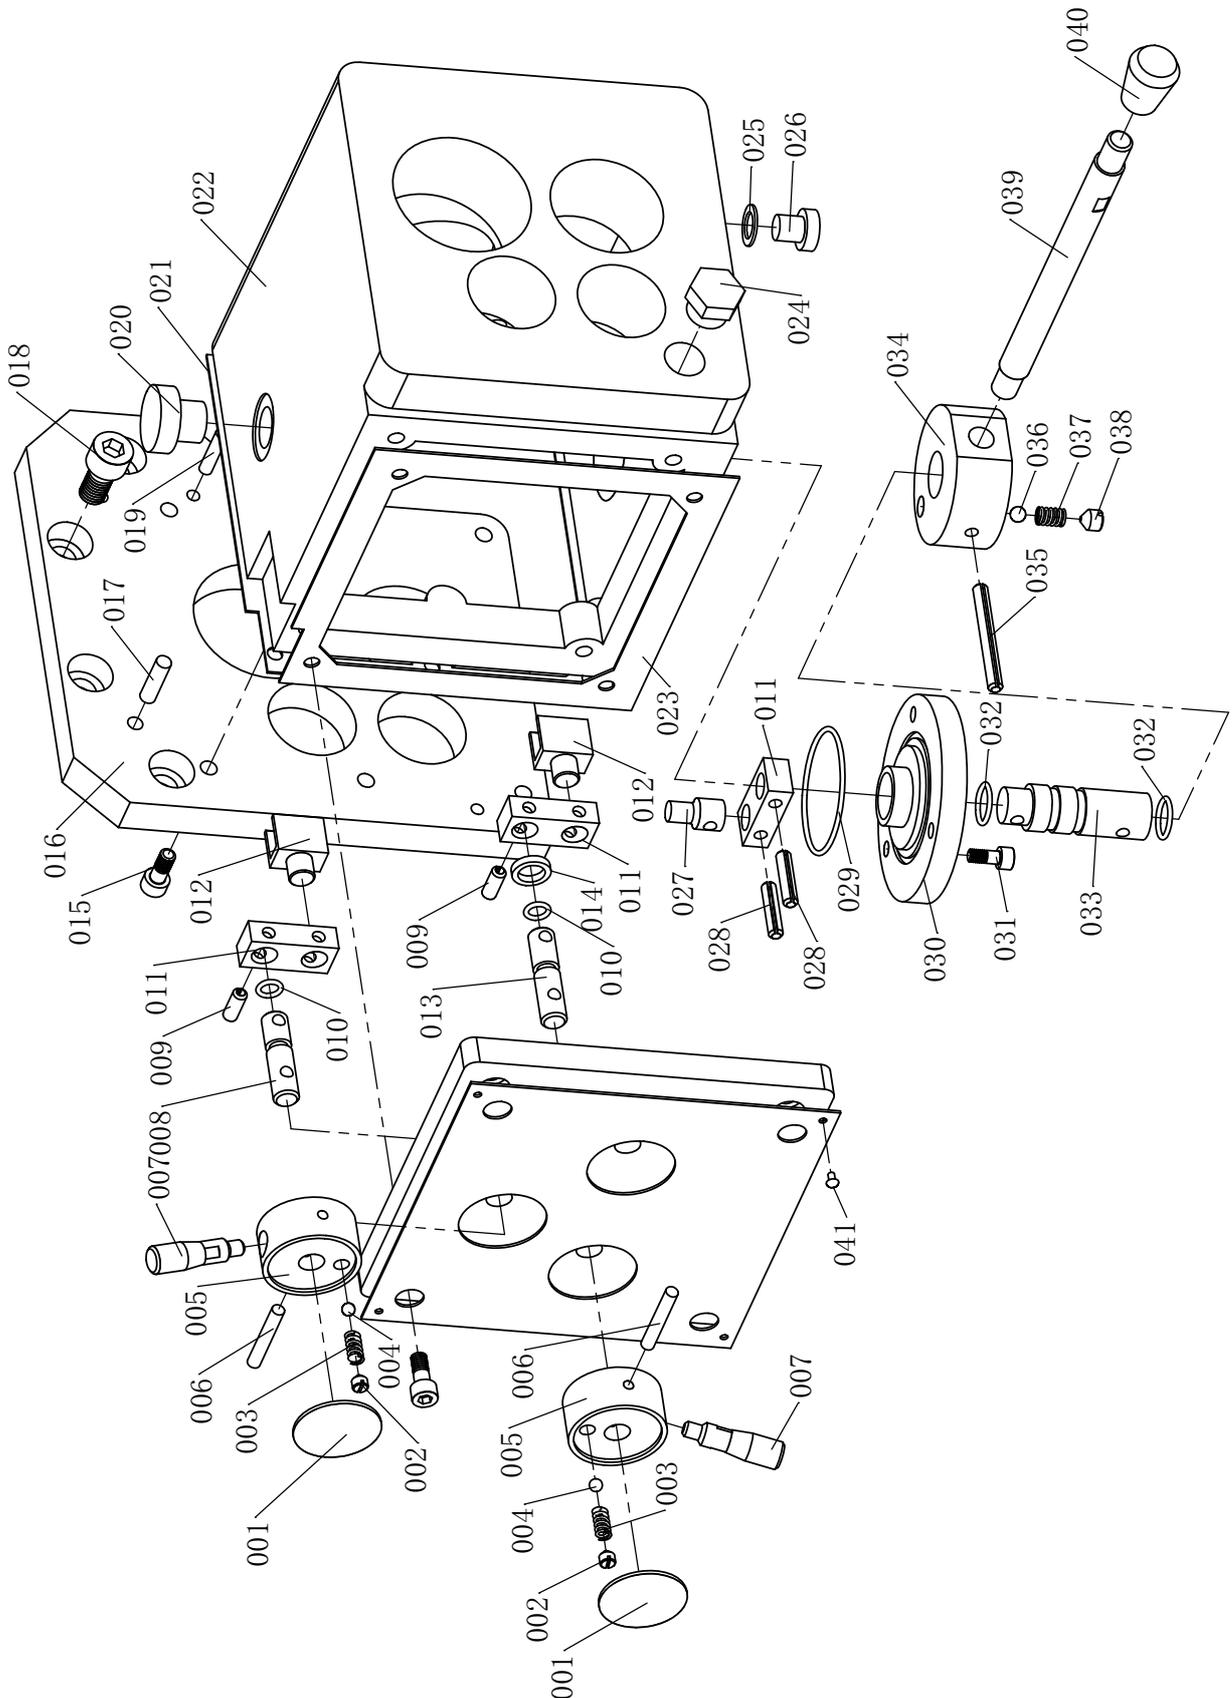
Vorschubgetriebe X-Achse - Feed gear X-Axis 1 - 3
